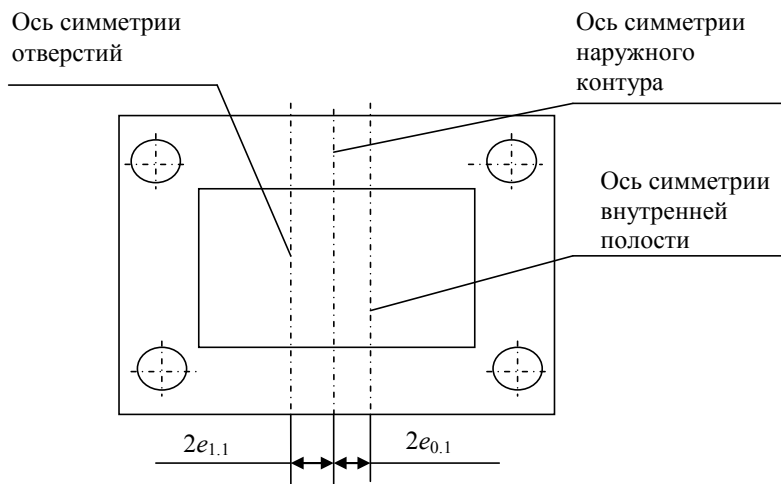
Смещение осей в заготовке и при обработке детали
